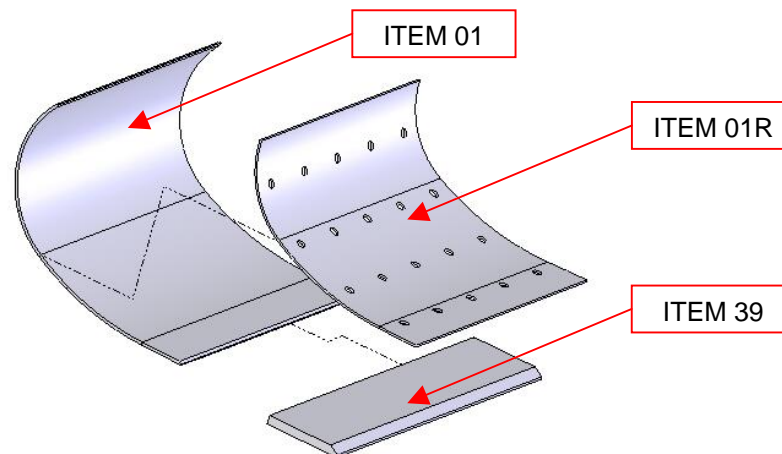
Vista explodida do subconjunto 01 - SC01.
